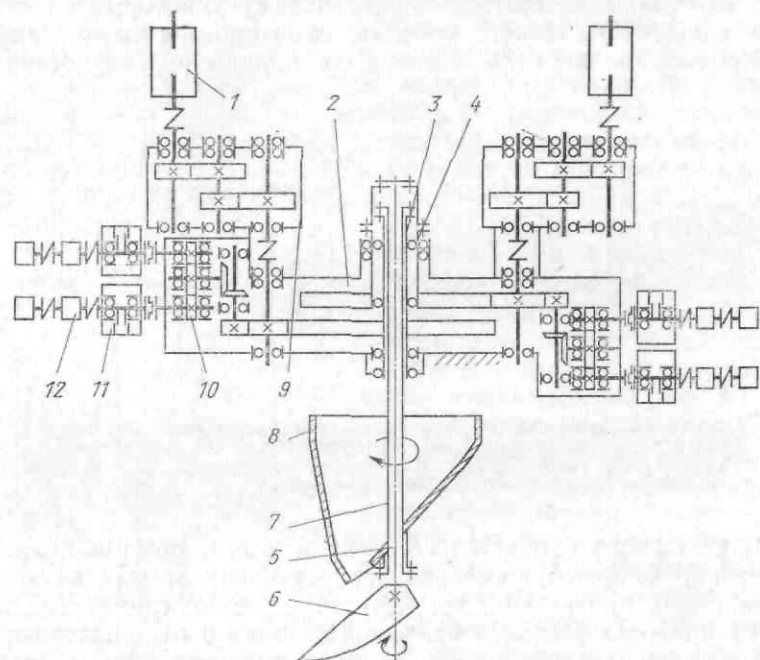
Кинематическая схема привода распределителя шихты бесконусного загрузочного устройства конструкции ВНИИметмаша — ПО «Уралмаш»: 1 — электродвигатель; 2 — тихоходный редуктор; 3 — выходной полый вал тихоходного редуктора; 4 — выходная втулка-стакан тихоходного редуктора; 5 — штанга склиза; 6 — склиз; 7 — штанга воронки; 8 — воронка; 9 — быстроходный редуктор; 10 — кинематический редуктор; 11 — бесконтактный путевой выключатель; 12 — сельсин-датчик
